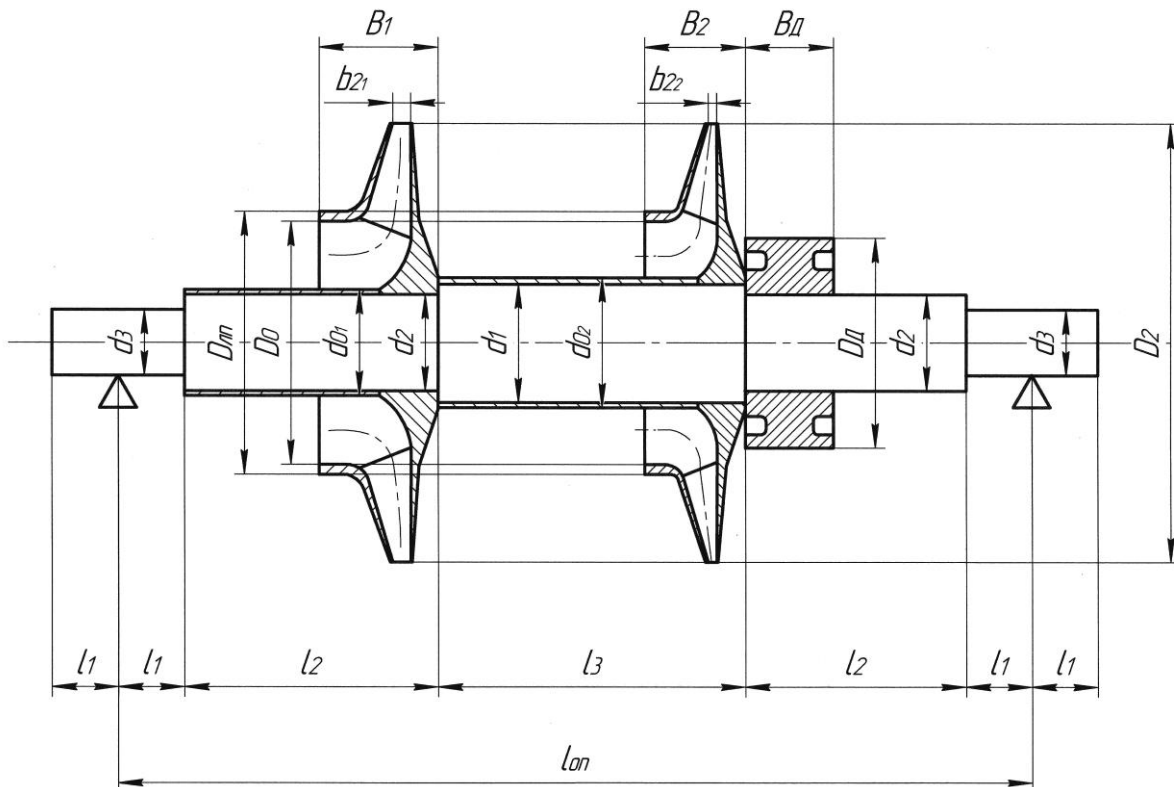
Размеры ротора двухступенчатого центробежного компрессора
